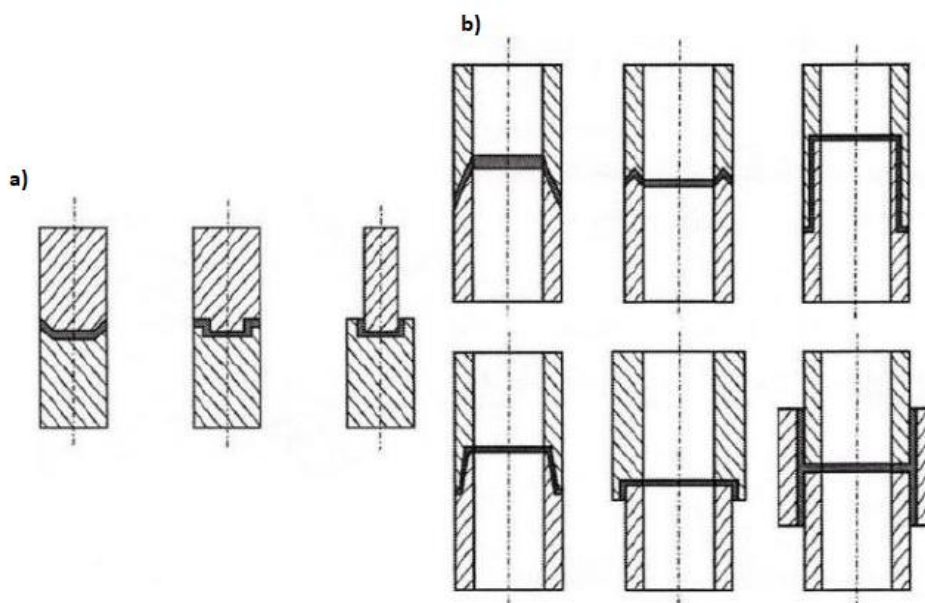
Configurações de juntas cilíndricas: a) Varões, b) Tubos [5].
